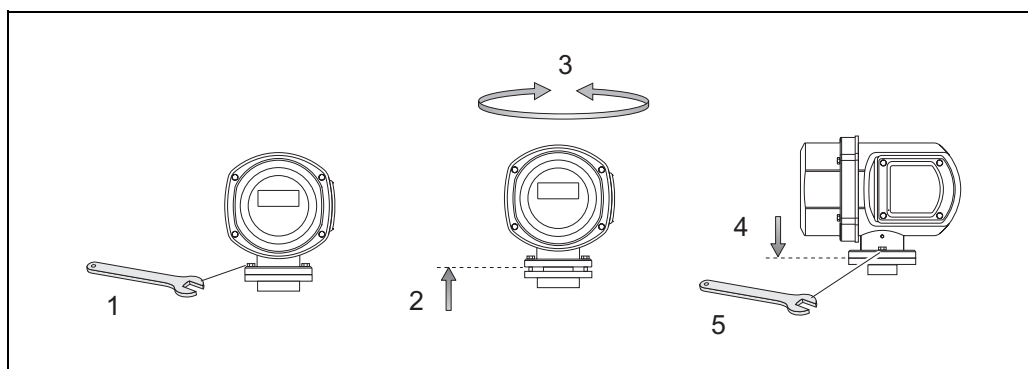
Поворот корпуса трансмиттера (корпус из нержавеющей стали)
